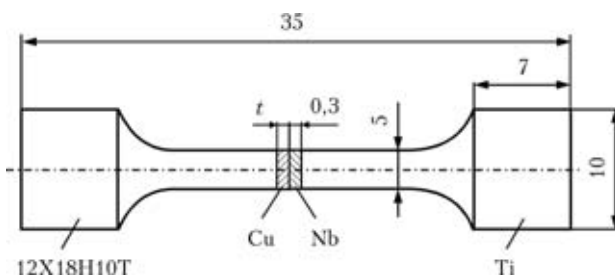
Схема образца для испытаний на разрыв материалов, сваренных в твердой фазе
